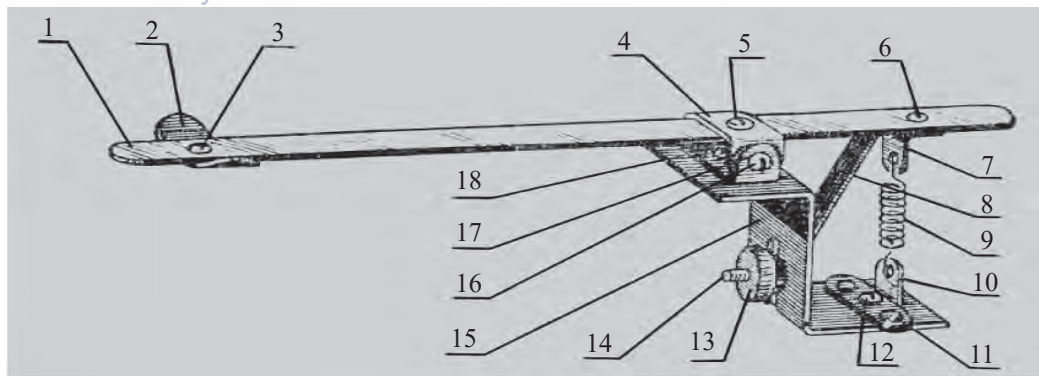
Строение соединительного механизма реле: 1 – якорь; 2 – контактная пластинка; 3 – заклепка; 4 – держатель якоря; 5, 6 – заклепки; 7 – верхний кронштейн; 8 – ограничитель; 9 – пружина; 10 – нижний кронштейн; 11 – заклепка; 12 – винт; 13 – гайка; 14 – винт; 15 – Z образная стойка; 16 – винт; 17 – стойка.
